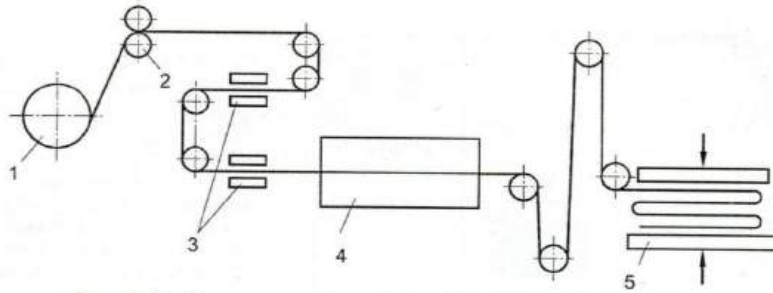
Схема виготовлення пакета стільникового заповнювача: 1 – рулонодержак; 2 – дискові ножі; 3 – клеянка; 4 – сушильна камера; 5 – пакетоукладач
